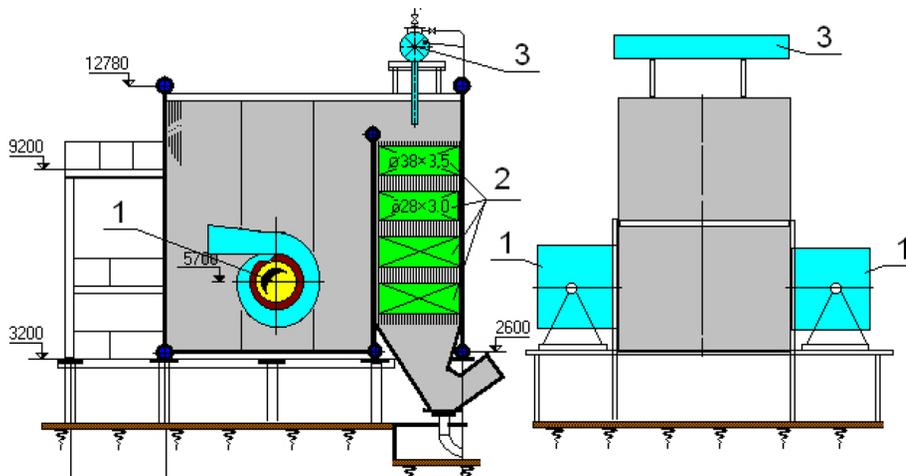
Водогрейный котёл КВГМ-116,3–150: 1 – ЦВП; 2 – конвективные поверхности нагрева
